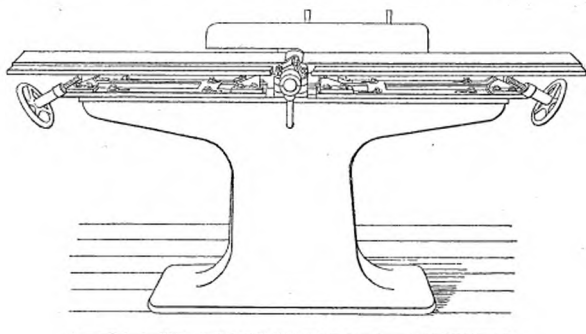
Machine à raboter et à faire les joints de la Egan Company.
